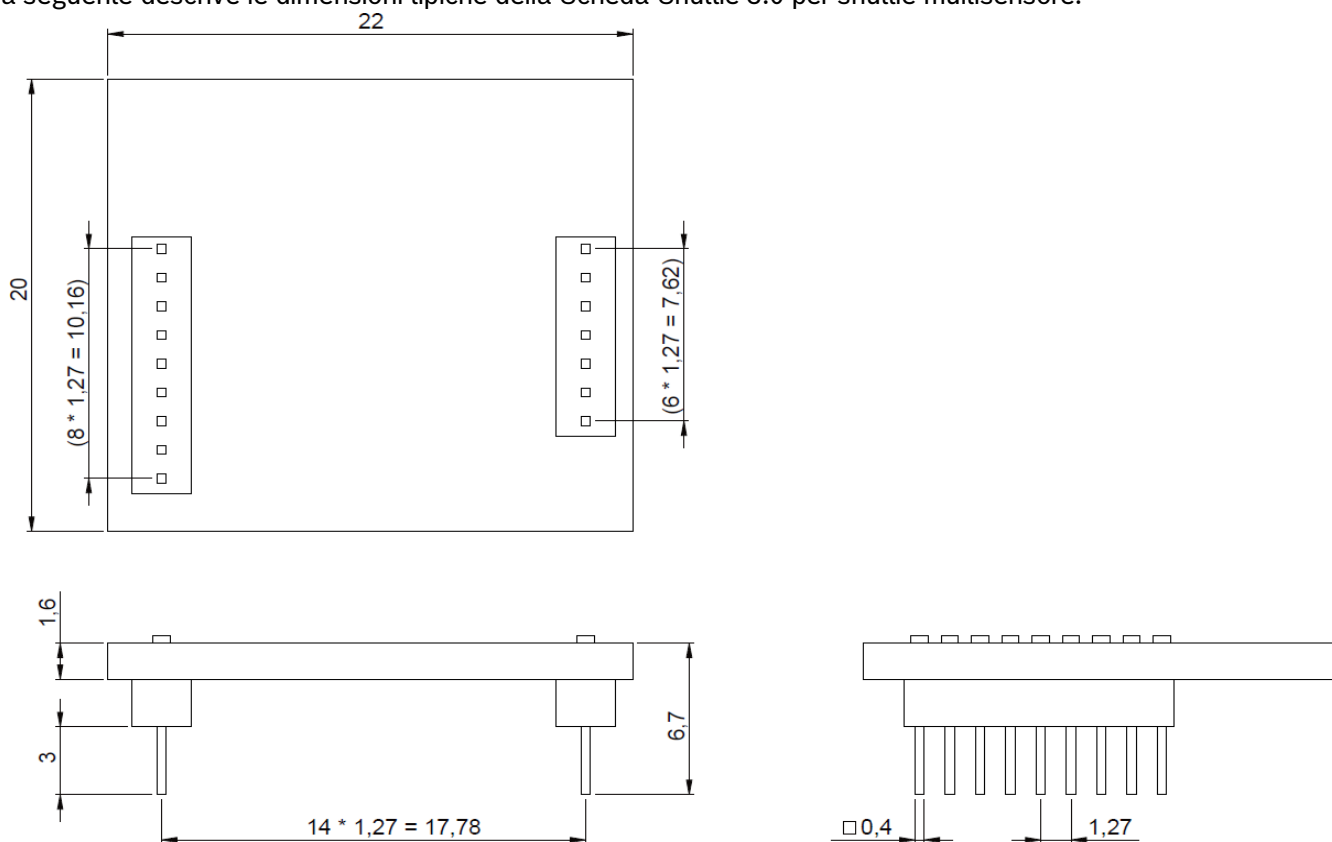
Dimensioni Scheda Shuttle 3.0 multisensore
